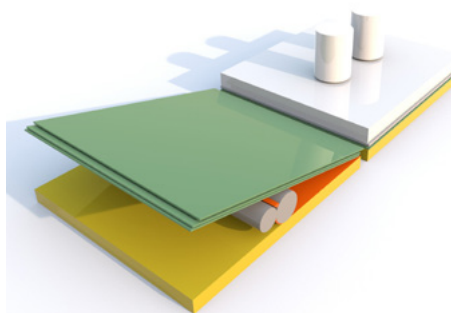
Pressa a piani con applicazione dell'adesivo con rulli direttamente sul pannello e applicazione del decorativo in fogli
